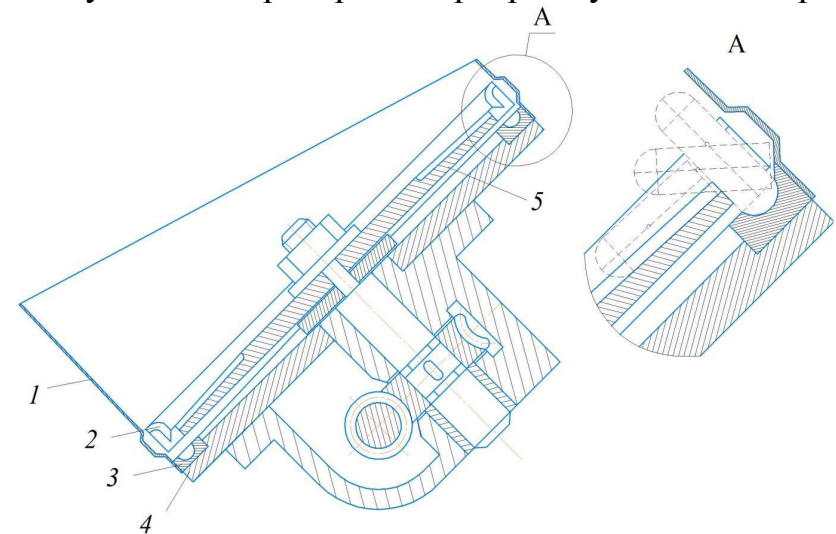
Зубчастий бункерний завантажувальний пристрій (удосконалений) для заготовок з відсутністю зміщення центру мас
